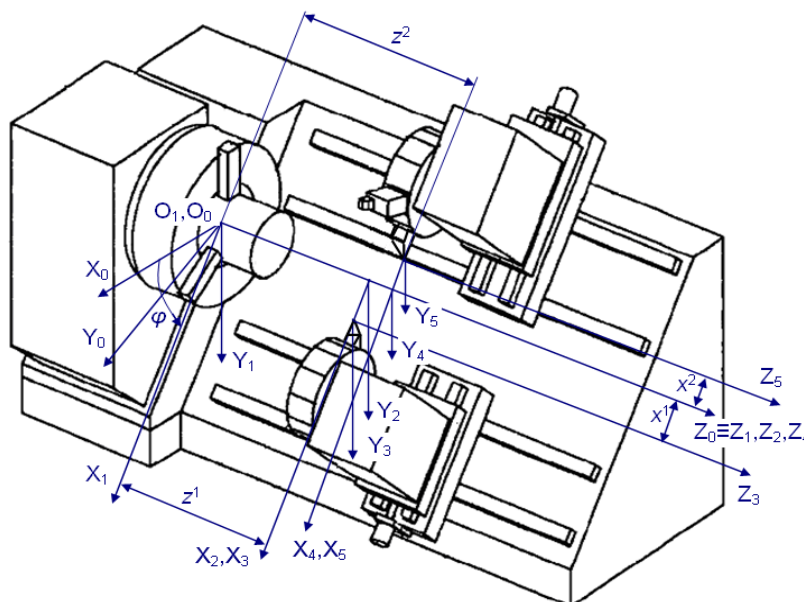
Формоутворююча система одношпindelного токарного верстата з ЧПК для паралельної токарної обробки
